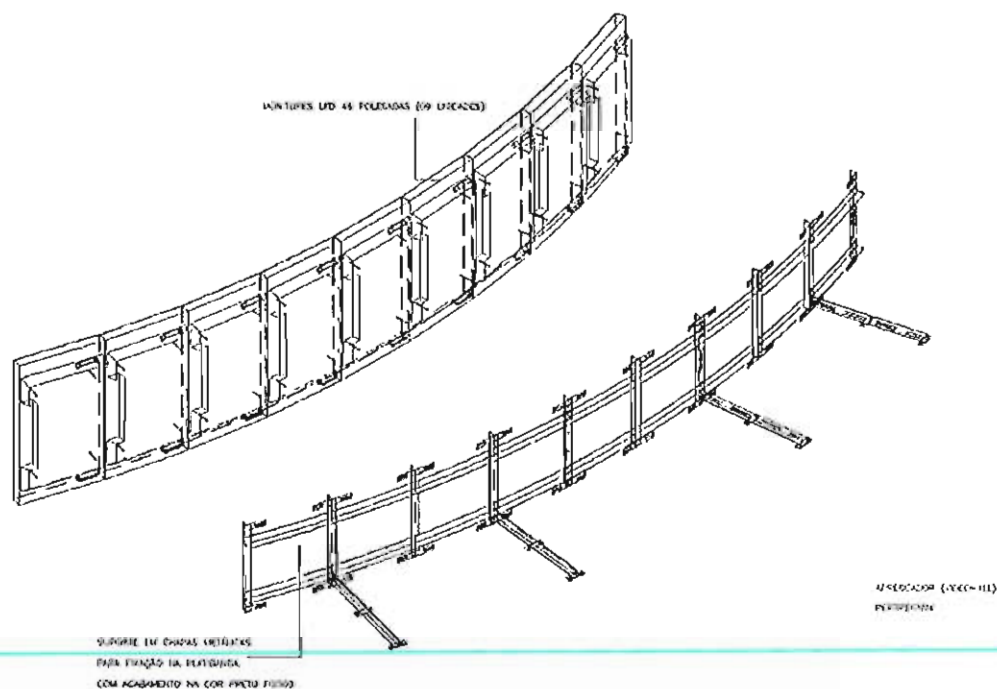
Estudo para a elaboração dos suportes dos painéis de Video Wall no Plenário.
